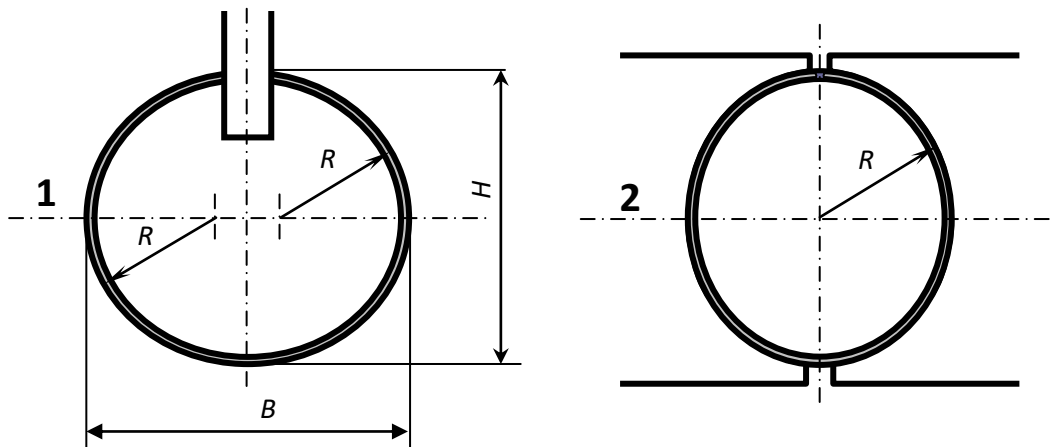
Схема формовки трубной заготовки в шовонаправляющей и шовообжимной клетях [23].
